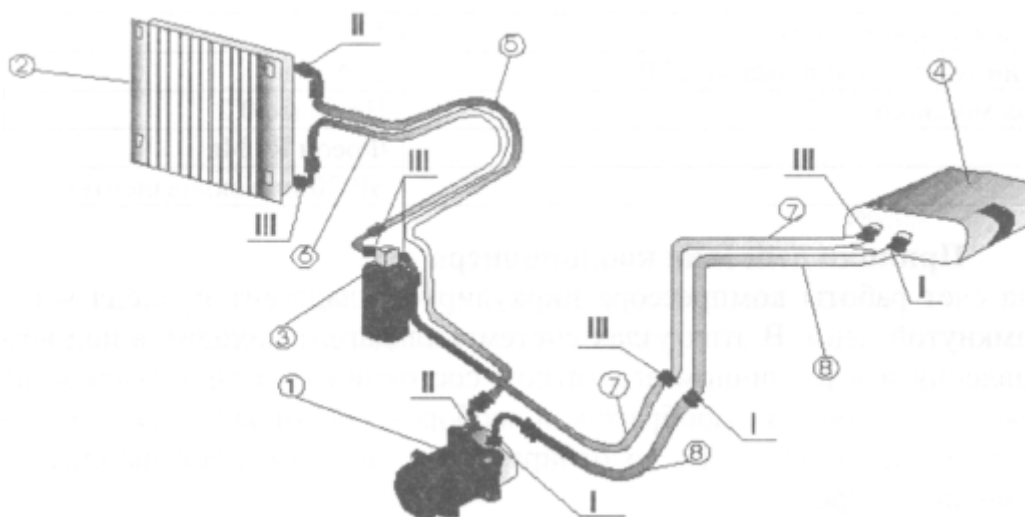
Принципиальная схема сборки кондиционера: 1 - компрессор с электромагнитной муфтой; 2 - конденсатора; 3 - ресивер осушителя с контрольным глазком и реле низкого и высокого давления; 4 - испаритель с вентиляторами обдува и панелью управления; 5 - трубопровод нагнетающий; 6 - трубопровод конденсаторный; 7 - трубопроводы высокого давления; 8 - трубопроводы низкого давления.
